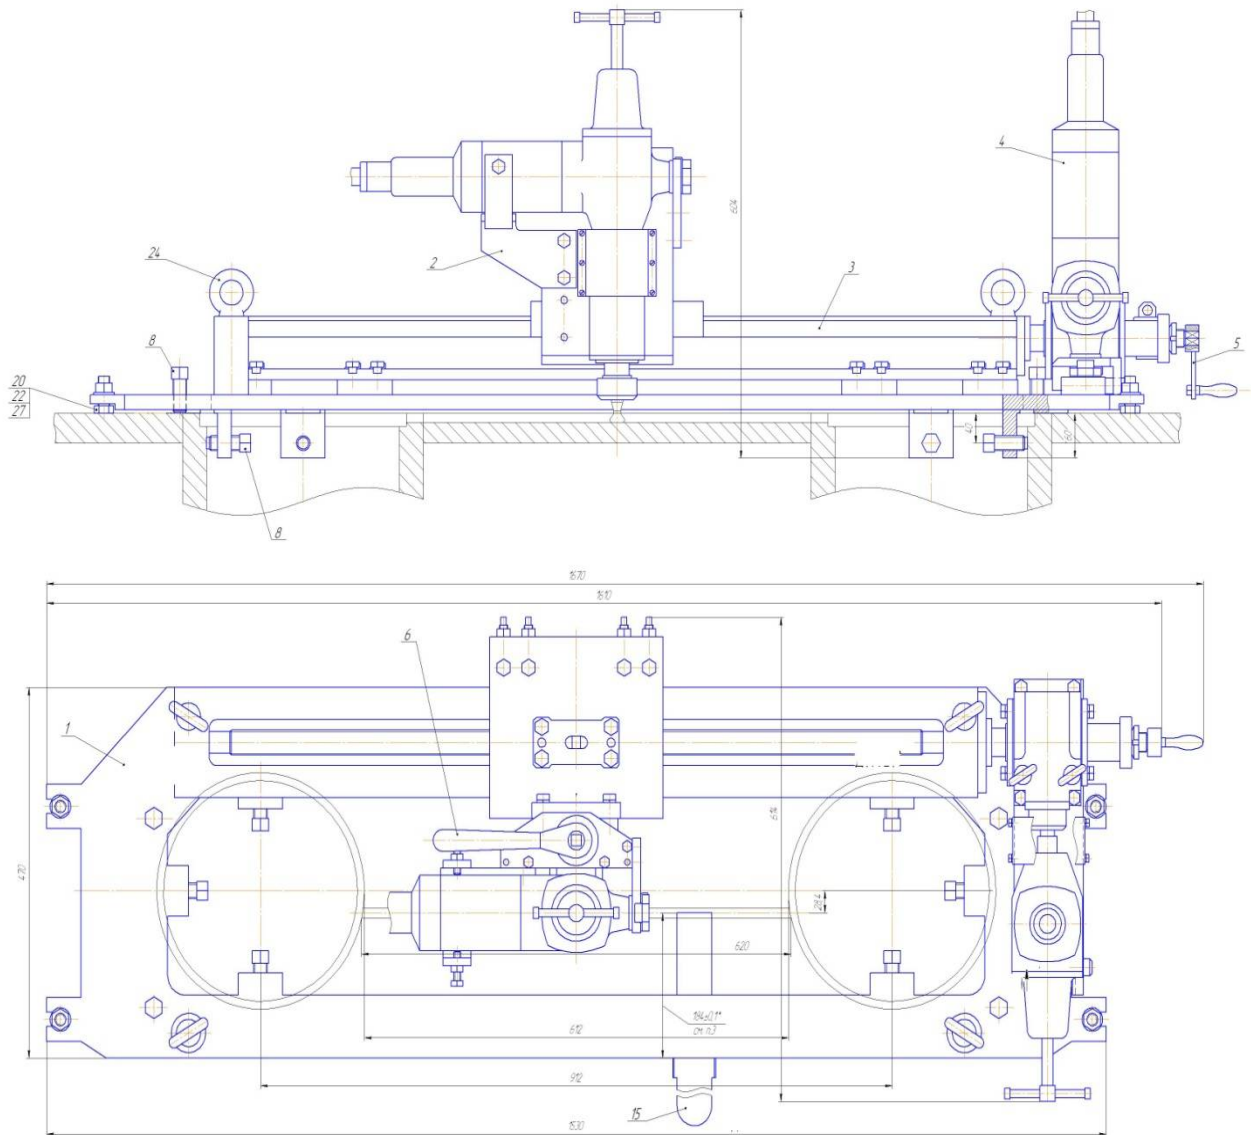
Компонівка OXZCу портативного станка для обработки паза
